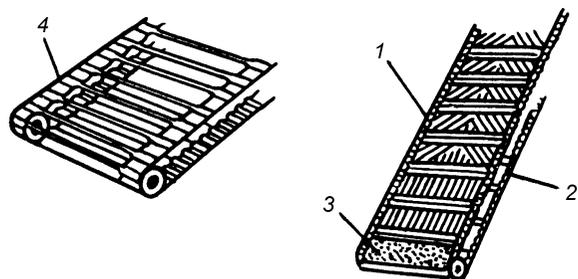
Сепарирующие органы [378]: 1 — сепарирующая решетка; 2 — цепочный транспортер; 3 — металлический лист; 4 — ленточный прутковый элеватор
